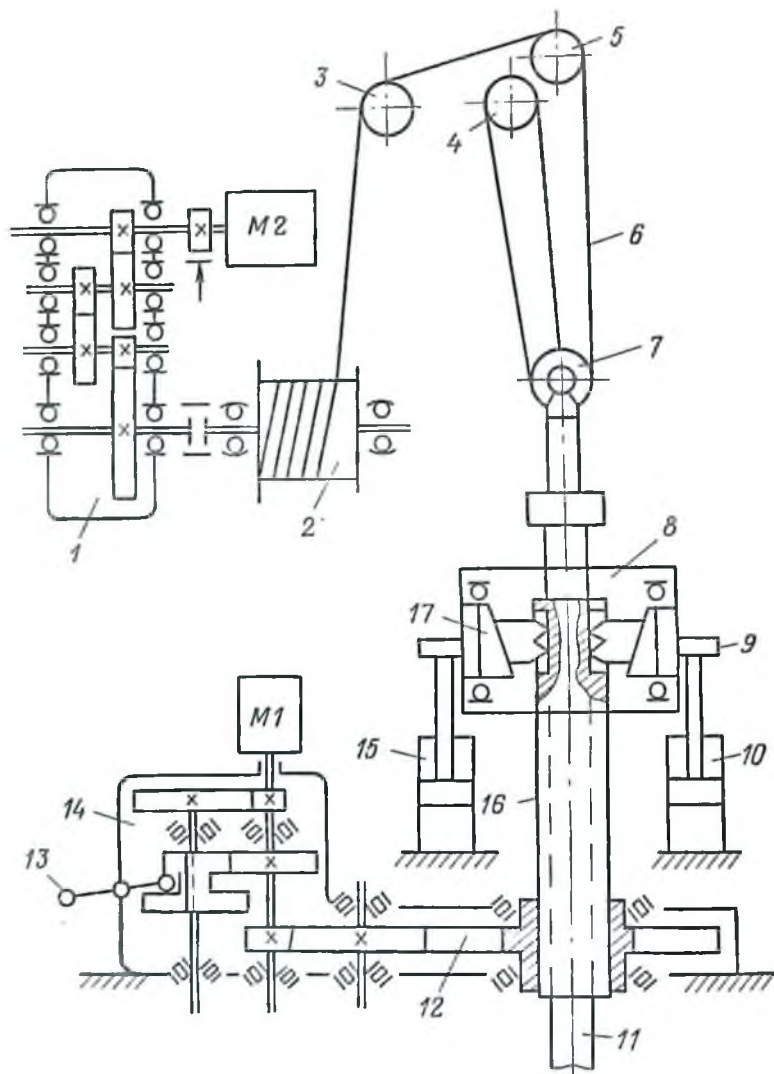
Кинематическая схема вращательно-подающего механизма патронного типа шарошечного станка 2СБШ-200-32
